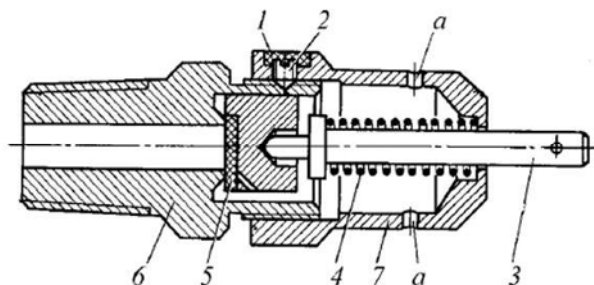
Предохранительный клапан: а -отверстия для выхода газа в атмосферу; 1- шайба; 2-стопорный винт; 3 - шток; 4 - пружина; 5 - клапан; 6- корпус; 7- крышка.
